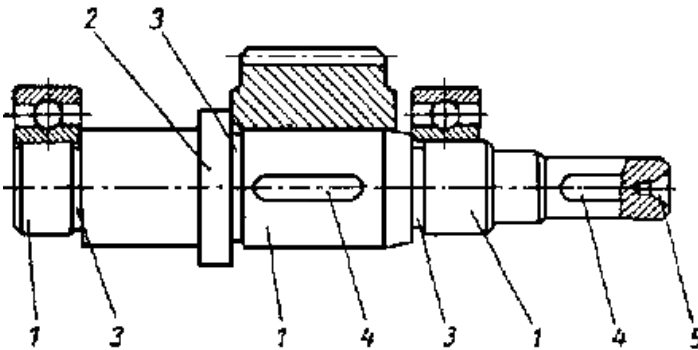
Вал редуктора у зборі з підшипниками і шестернею
